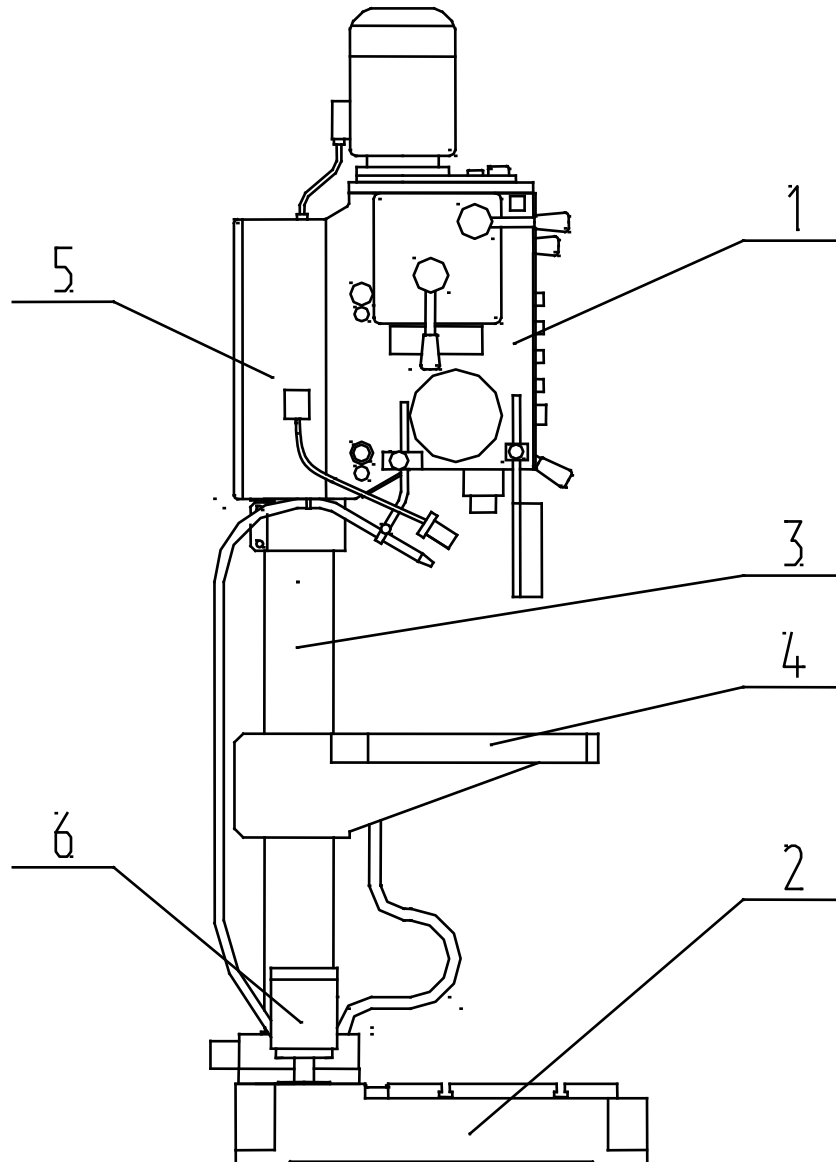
Общий вид станка вертикально-сверлильного модели 2Т125
